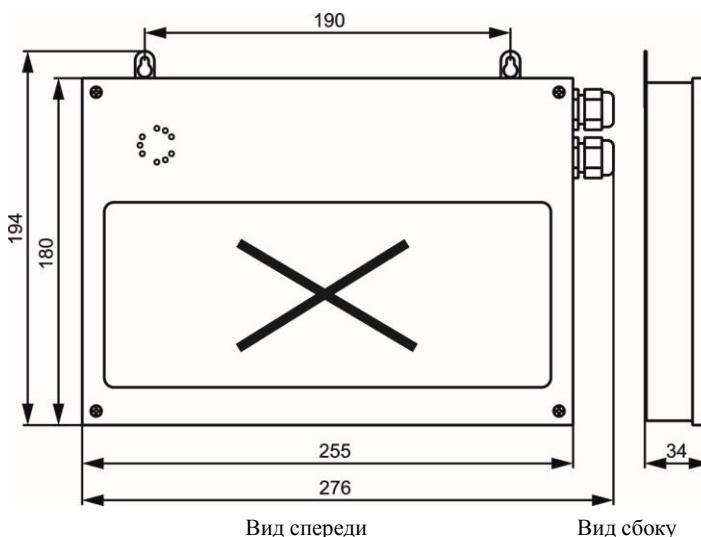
Внешний вид, габаритные и установочные размеры корпуса оповещателя
